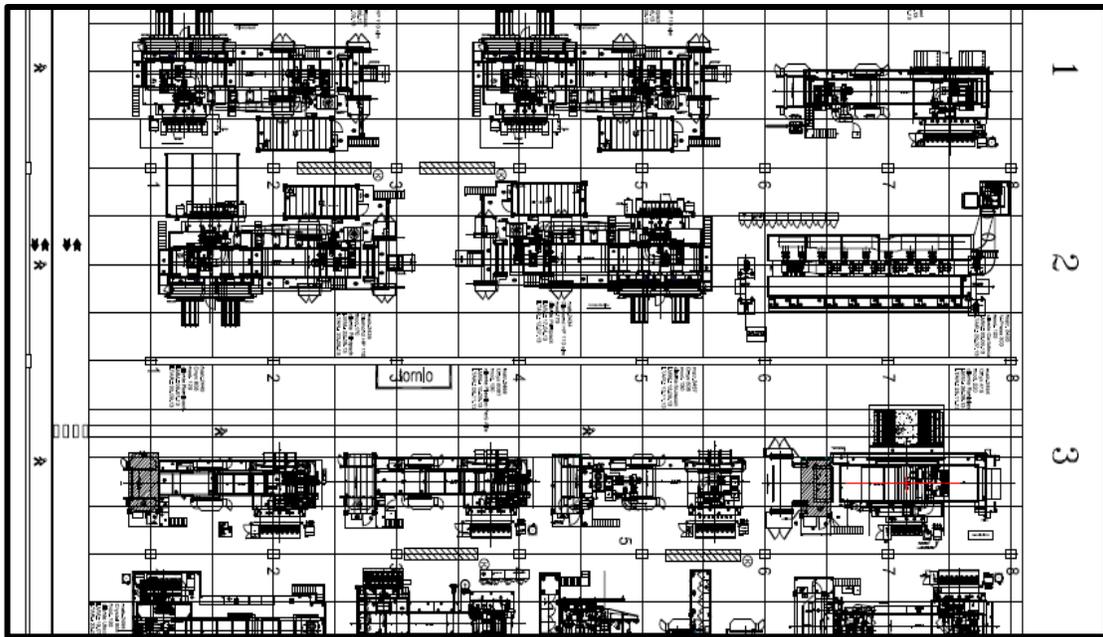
Layout disposizione macchine nelle varie campate del capannone.
